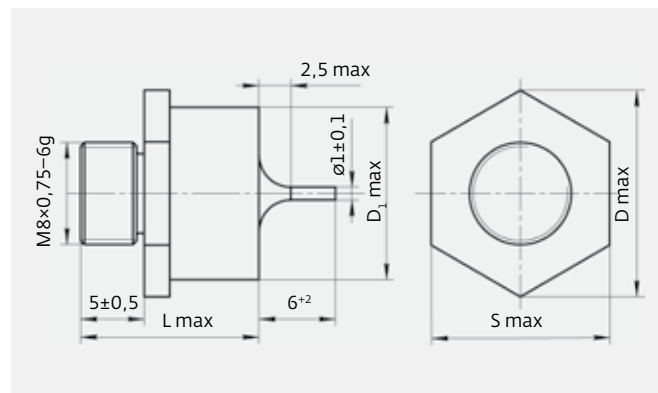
Конструкция и размеры (см. табл.1) конденсаторов с номинальным напряжением 500, 750 и 1000 В
